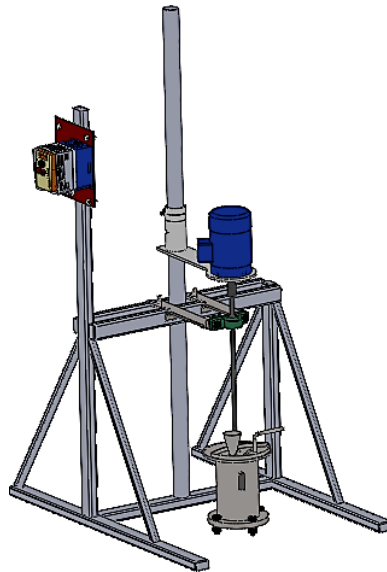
Ensamble final de partes y elementos diseñados.
